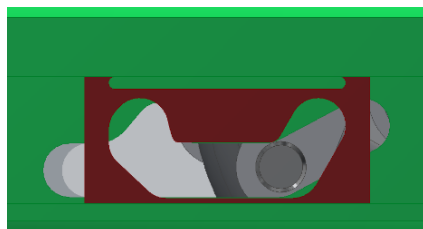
Detail konstrukčního řešení obrázku 3.2
